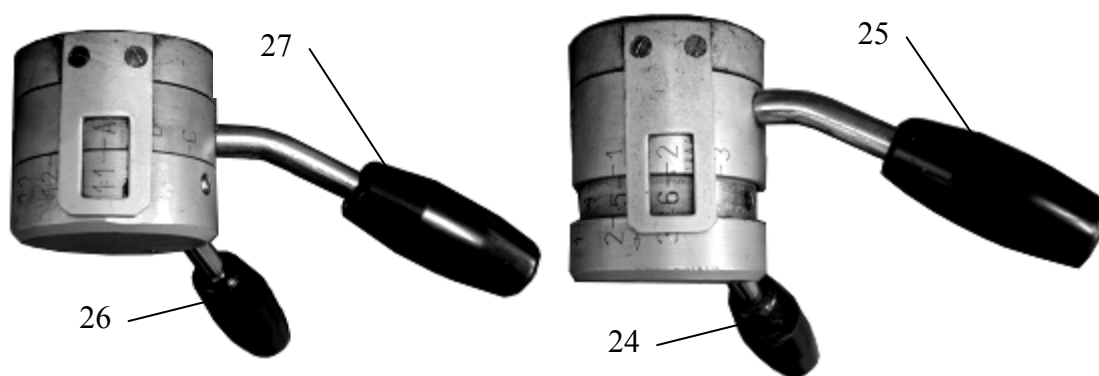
Рукоятки настройки величины подачи или шага нарезаемой резьбы
